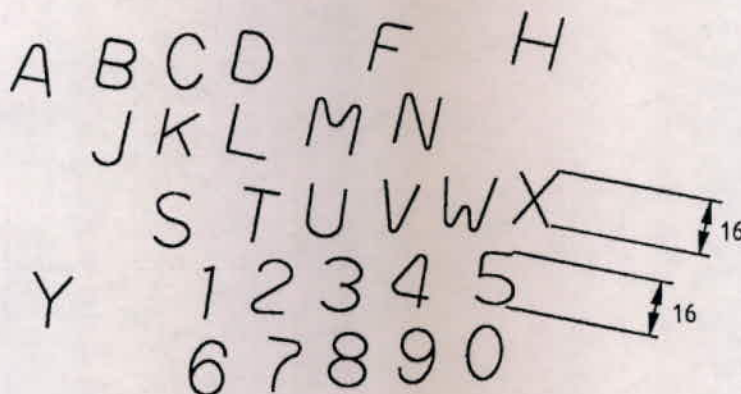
Diseño de letras y números inclinados 10° para estampado en carriles
